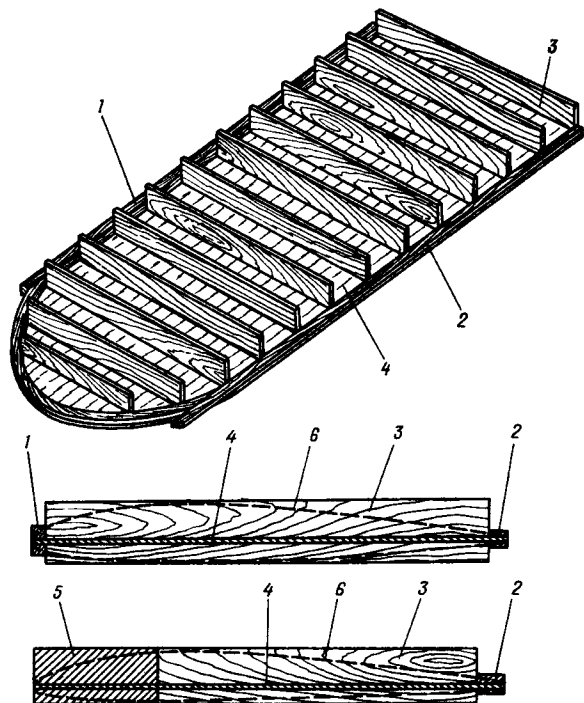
Изготовление крыла макета под мягкую обшивку:
